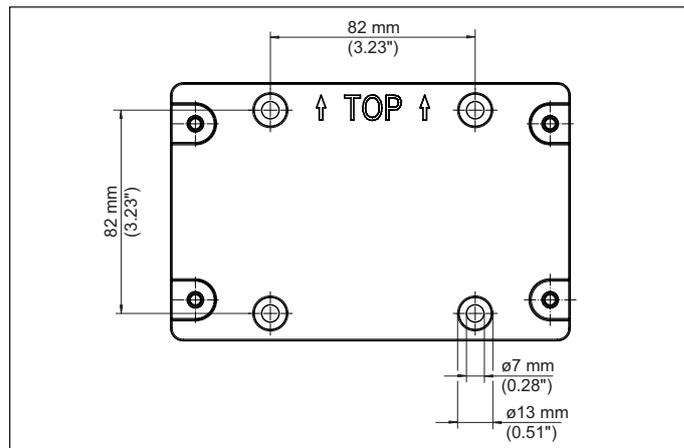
Placa de montaje para montaje en pared (VEGAMET 841, 842)
